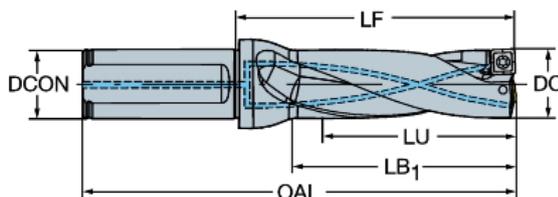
Сверло со сменными пластинами CoroDrill® 880-D2200L25-03
